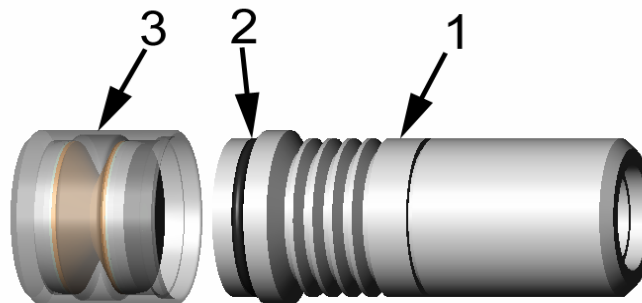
Vue éclatée, dimensions 1,560 po (39,62 mm) - 2,125 po (53,98 mm)
